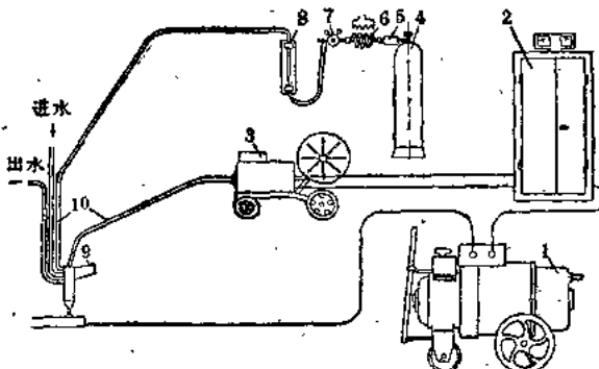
二氧化碳气体保护半自动焊接装置示意图
